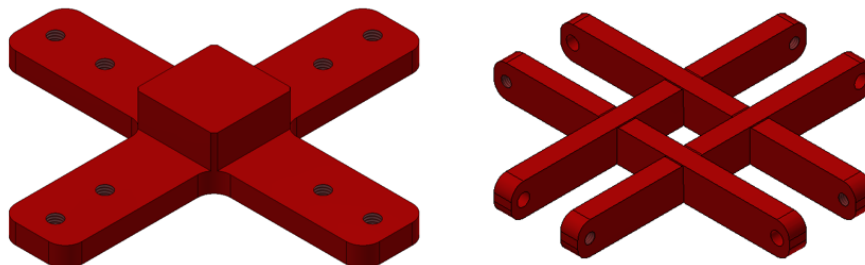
Supporto inferiore (a sinistra) e supporto superiore assemblato (a destra)
